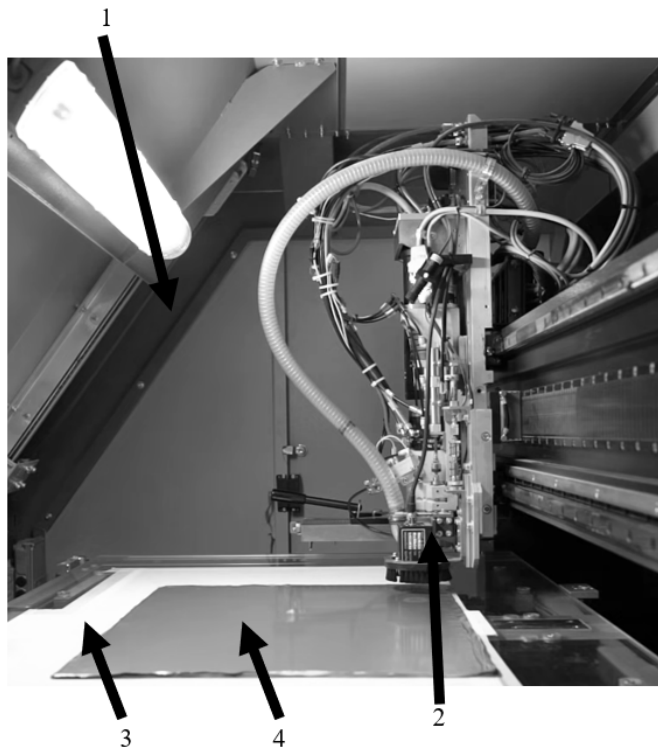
Сверлильный станок с автоматической сменой сверл:
